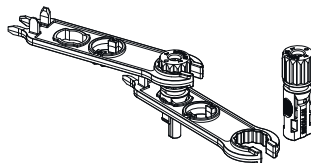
Соединитель с навинченной колпачковой гайкой
